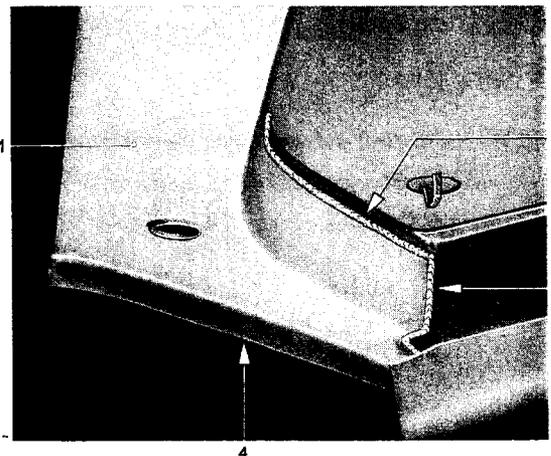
Innenseite der rechten Seitenstrebe an Seitenstrebenrest und hinteren Motorquerträger lichtbogengeschweißt – Linke Seitenstrebe in gleicher Weise lichtbogenschweißen
